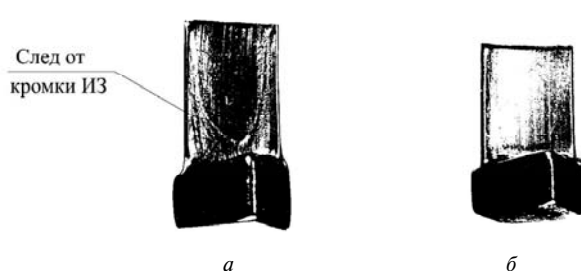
Внешний вид заготовок лопатки 6 степени компрессора, выдавленных из серийной заготовки (*а*) и заготовки с радиусом по торцу $R4$ (*б*)
